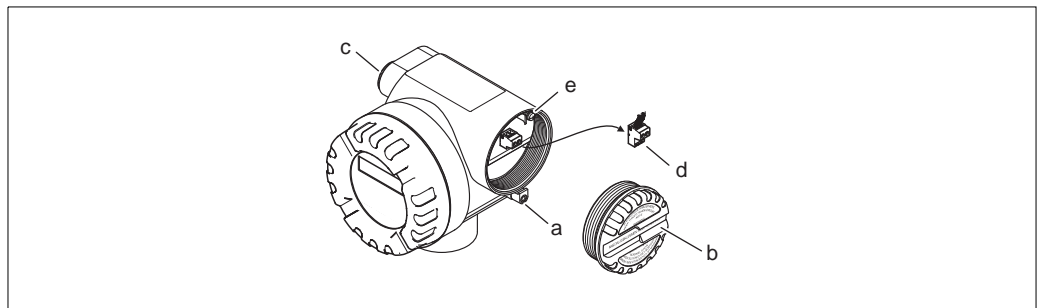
Anschluss des Messumformers Ex d Ausführung
